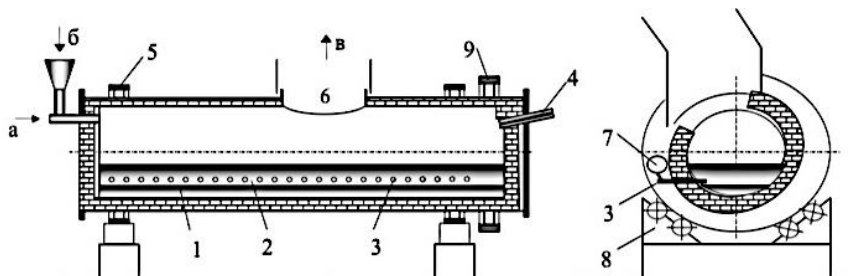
Конвертер в рабочем положении [17]:
